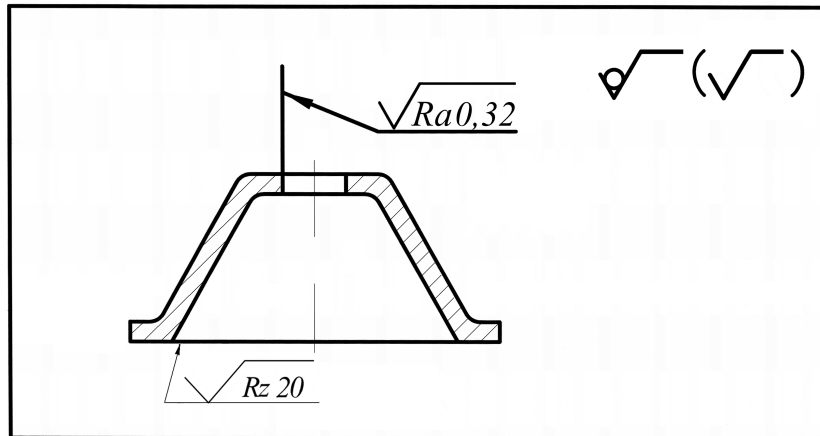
Обозначение шероховатости для детали, имеющей необработанные поверхности
